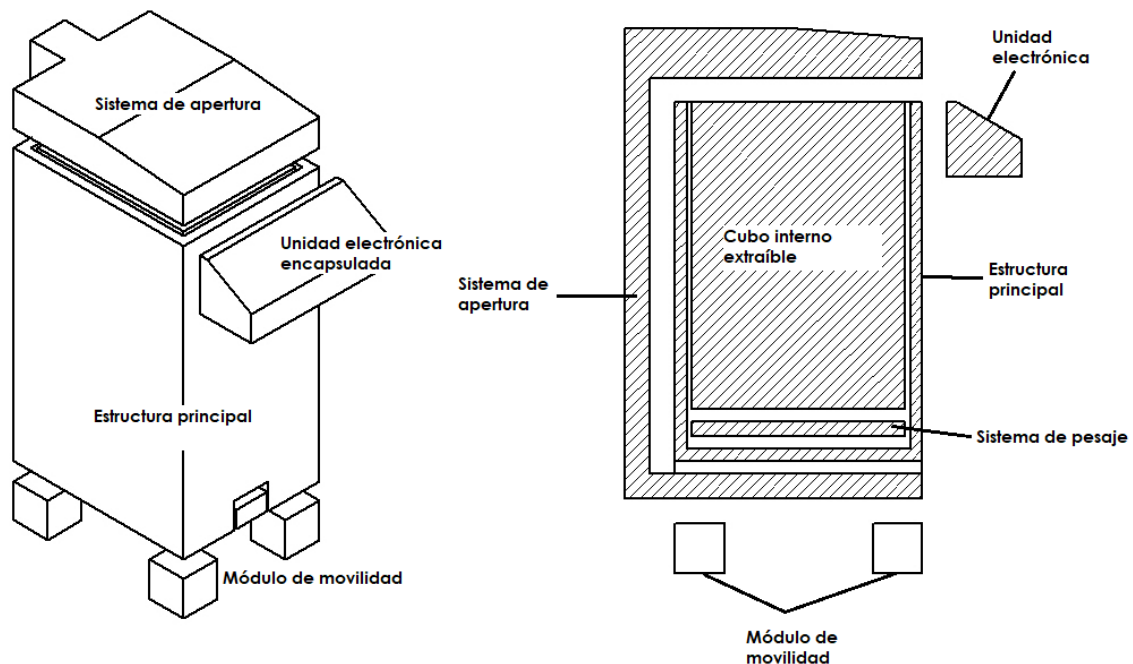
Representación geométrica inicial. Fuente: Primaria.
